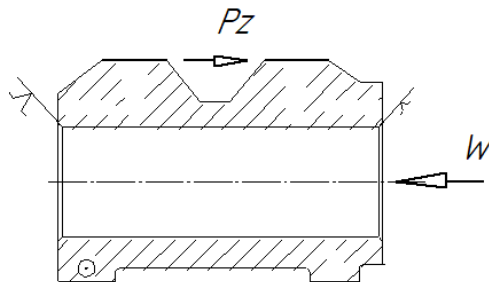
Схема базування та закріплення при фрезеруванні
